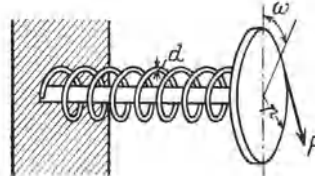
Schraubenfeder mit kreisförmigem Querschnitt.
